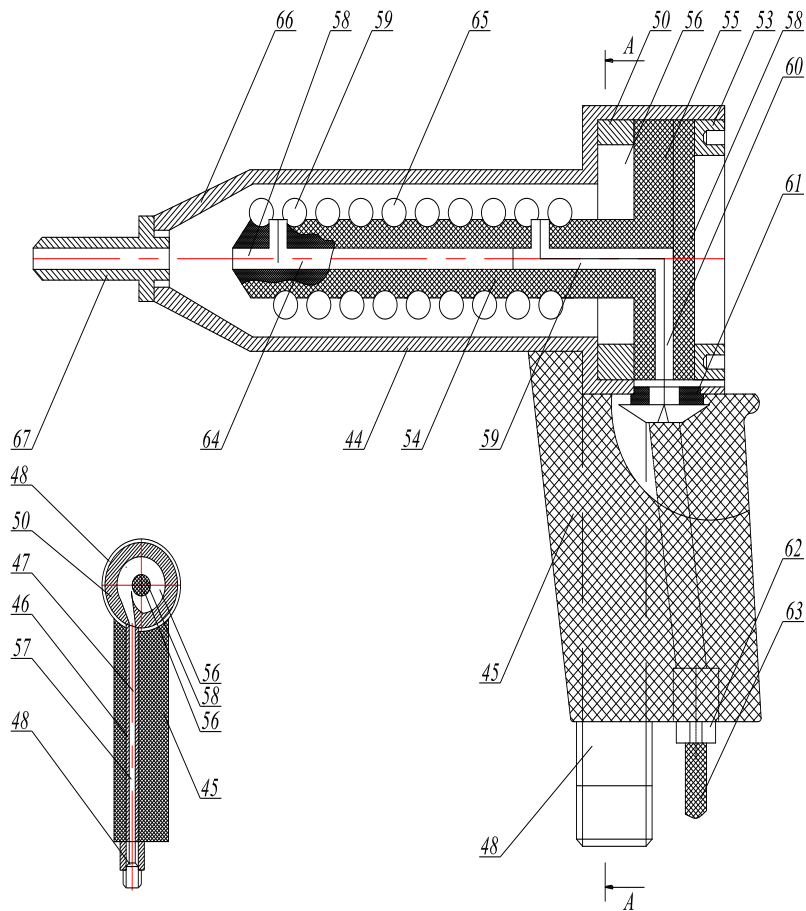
Пристрій для зварювання термопластів із нагрітим газом
